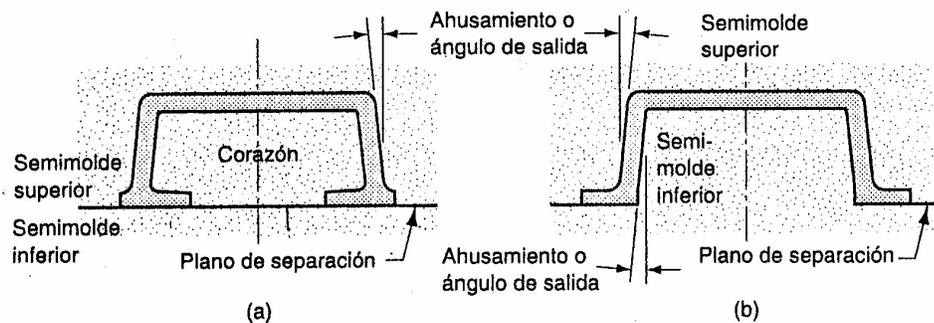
Cambio de diseño para eliminar la necesidad de usar un corazón: (a) diseño original y (b) rediseño.
